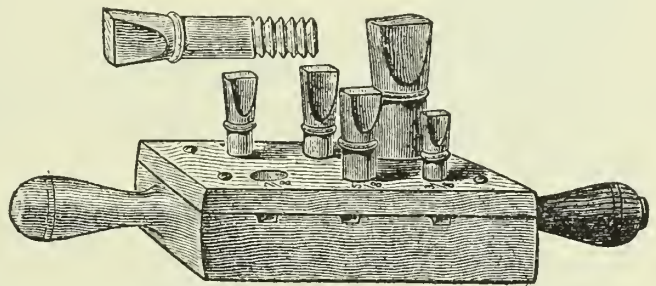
Holzschrauben-Schneidzeug für sechs Gewinde.
